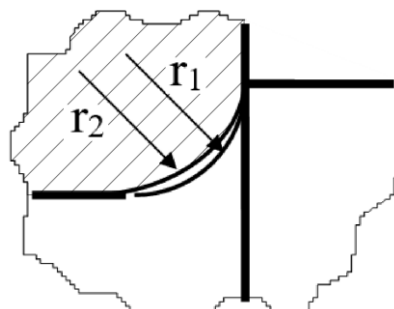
Сопряжение закруглений подшипника и вала
